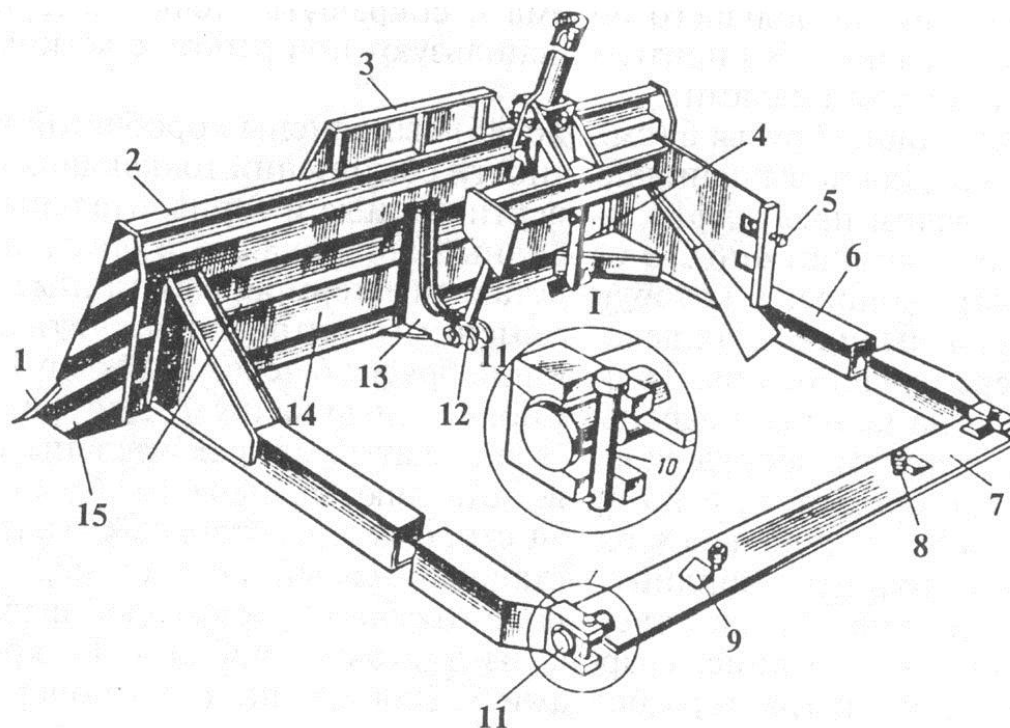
Конструкция бульдозерного оборудования с жестким креплением отвала к толкающим брусьям: 1 – нож, 2 – отвал, 3 – козырек, 4 – фиксаторы транспортного положения оборудования и балки, 5 и 8 – болты, 6 – толкающий брус, 7 – поперечная балка, 9 – фиксатор, 10 – палец, 11 – вкладыш, 12 – гидроцилиндр, 13 – кронштейн, 14 – пояса жесткости, 15 – боковая щека
